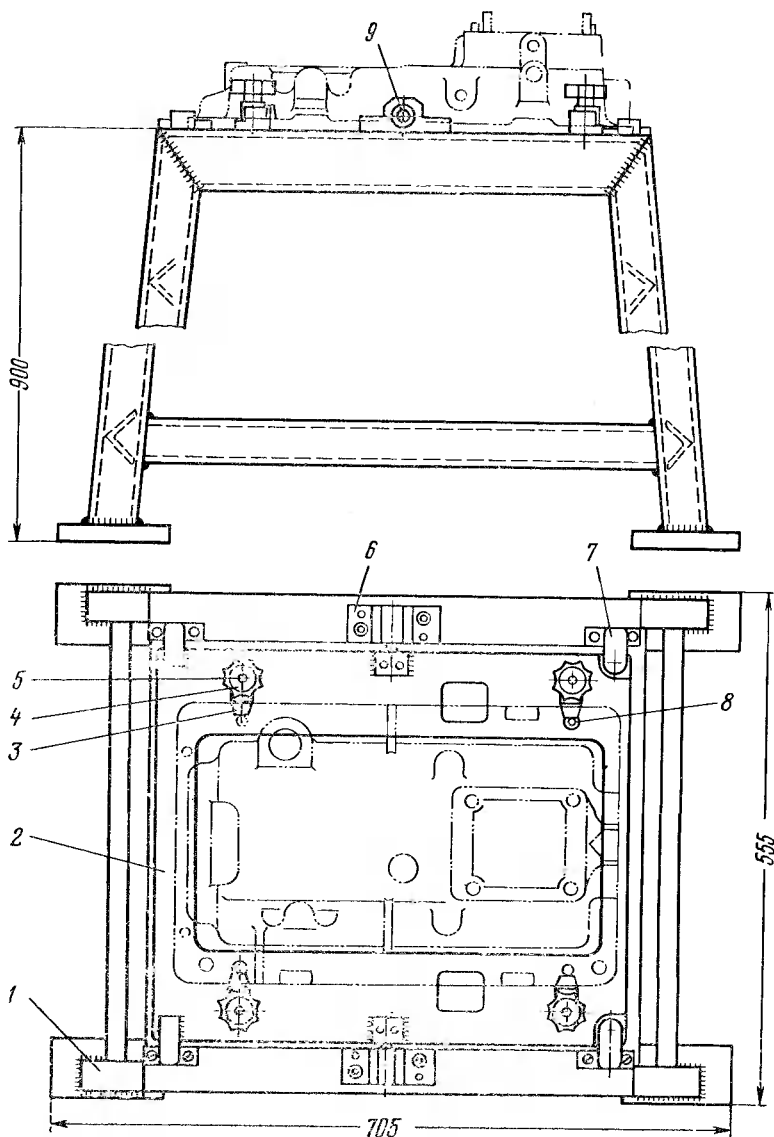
Приспособление для разборки и сборки верхней крышки коробки передач:
